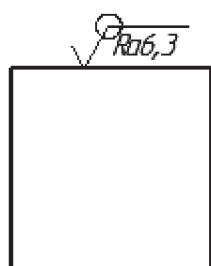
Обозначение шероховатости поверхности, одинаковой по всему контуру детали
